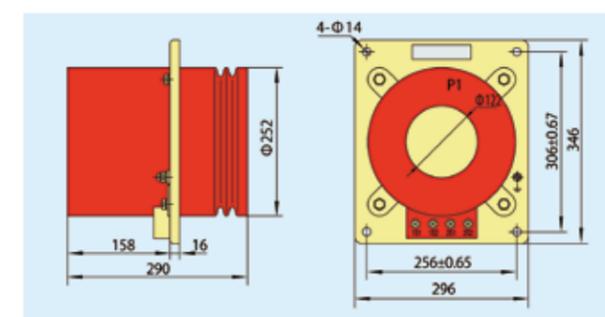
Внешний вид и размеры трансформатора тока LAJ-10(Q) 1000~2000 А
